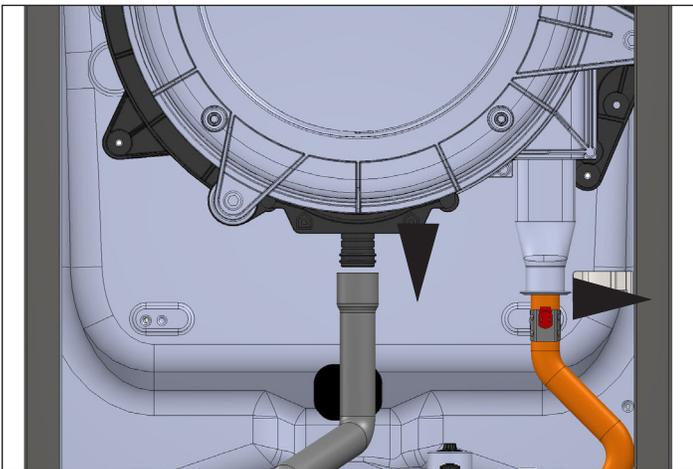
Retrait du conduit des condensats et du conduit de retour du chauffage central
